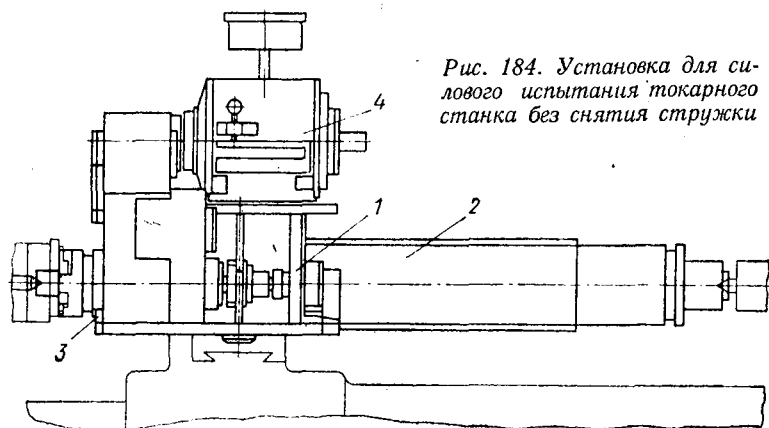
Установка для силового испытания токарного станка без снятия стружки
